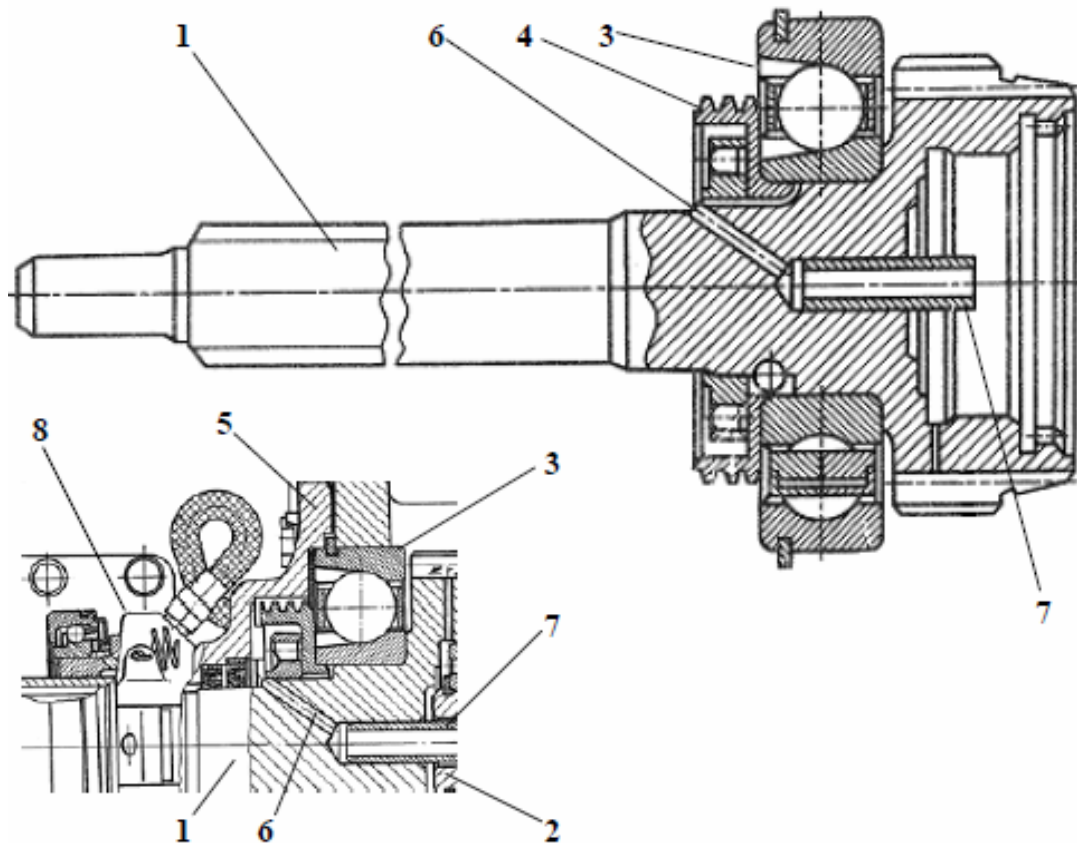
Система принудительной смазки некоторых сопряжений в коробках передач КАМАЗ:
